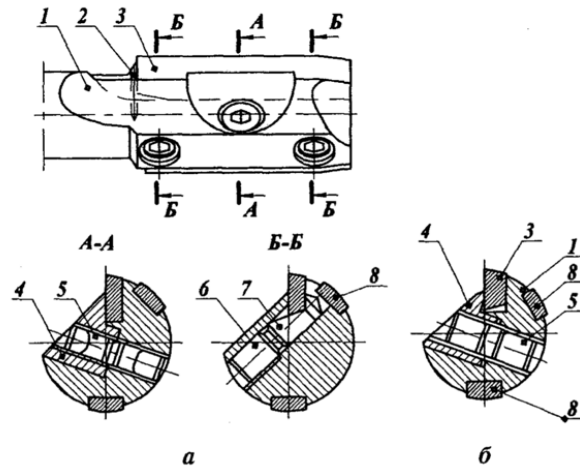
Однолезові розвертки зі змінною твердосплавною пластиною
